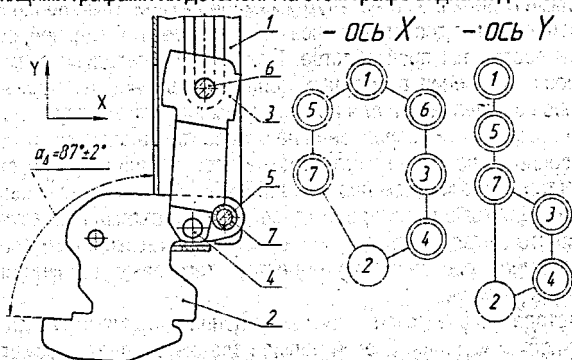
Эскиз сборочной единицы и графа деталей:
